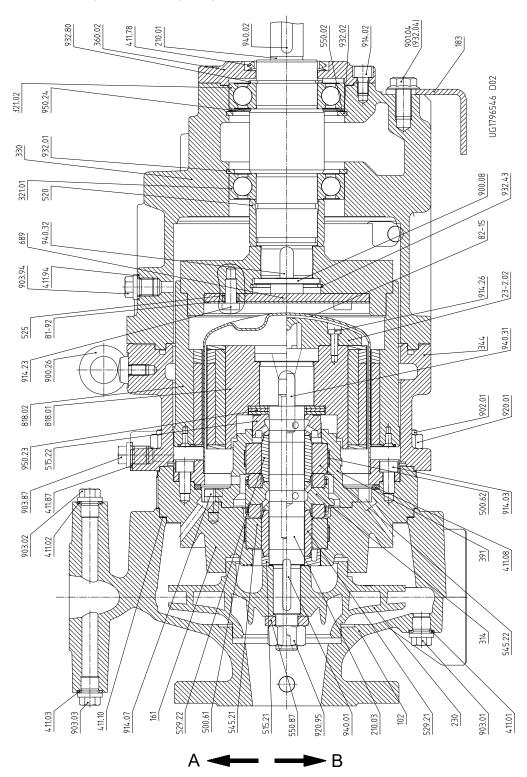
Gesamtzeichnung Ausführung mit geklemmtem Deckel ohne Zwischenstück
